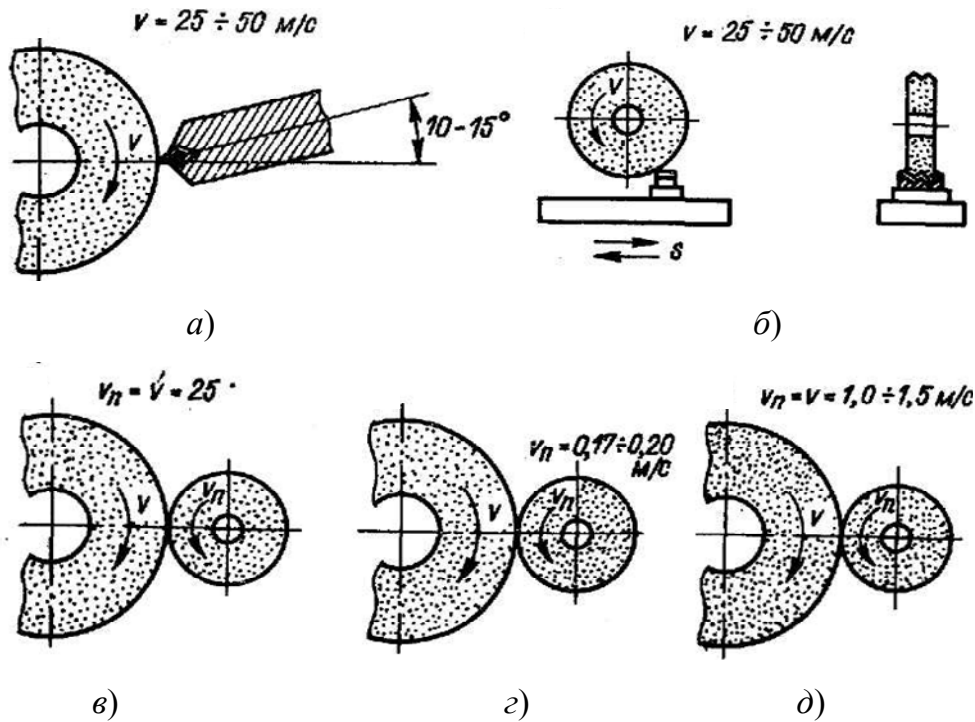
Схемы методов правки шлифовальных инструментов: а – обтачиванием (точение радиальное); б – тангенциальным точением; в – обкатыванием; г – шлифованием; д – накатыванием
